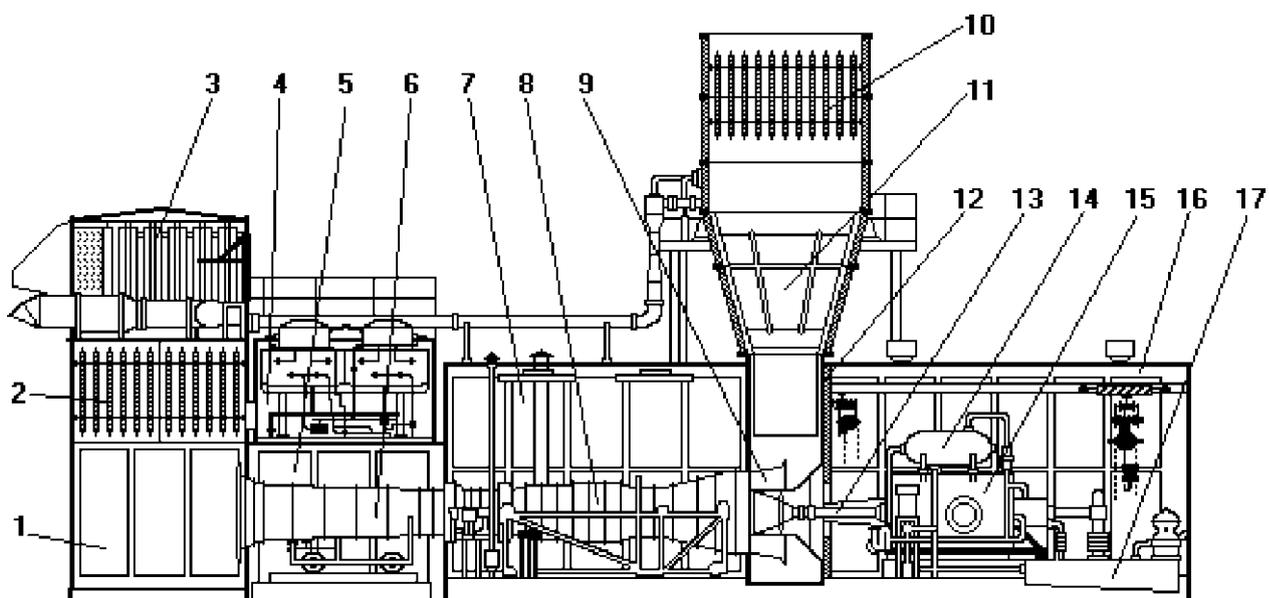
Компоненка агрегата: 1-камера всасывания; 2- шумоглушители; 3-воздухоочистительное устройство; 4-блок вентиляции; 5- промежуточный блок; 6-патрубок; 7-отсек двигателя; 8-двигатель НК-16СТ; 9- выхлопная улитка; 10-шумоглушители выхлопа; 11-диффузор; 12-герметичная перегородка; 13-промежуточный вал; 14-гидроаккумулятор; 15-нагнетатель НЦ-16;16-отсек нагнетателя; 17-маслобак нагнетателя
